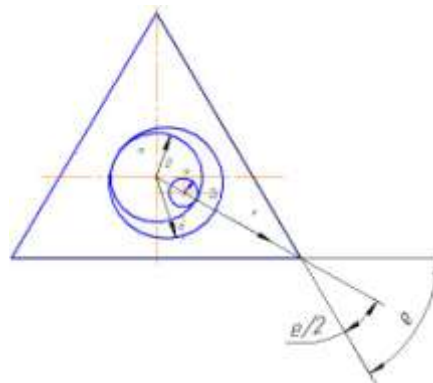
Расчетная схема эксцентрического закрепления
